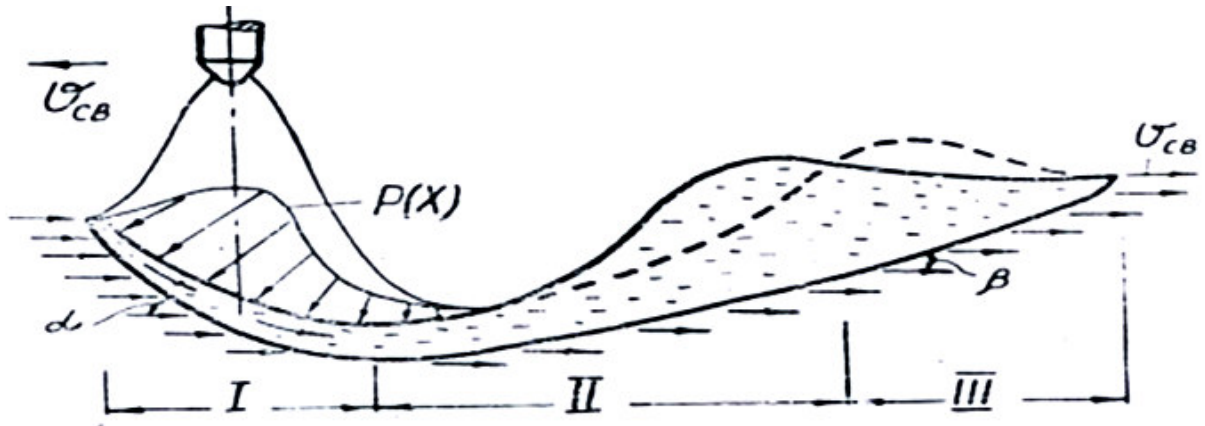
Гидродинамическая модель сварочной ванны
